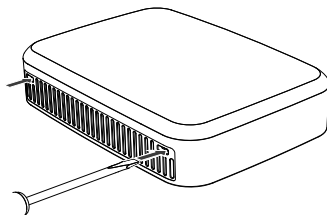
Desmontaje tapa frontal / Front cover dismounting /
